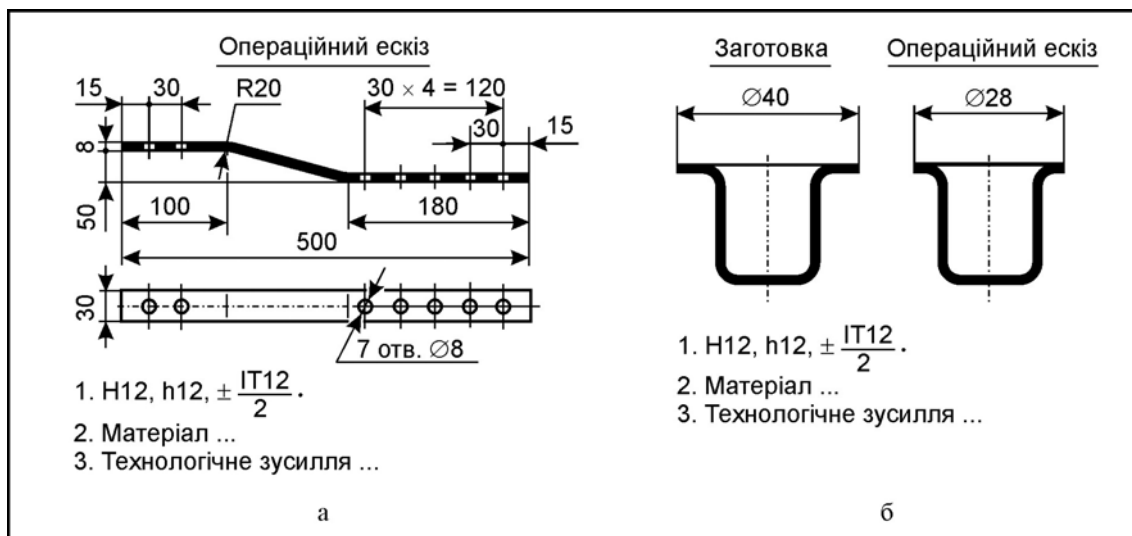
Приклади оформлення операційних ескізів: а – операційний ескіз деталі «Планка» штампа для пробивання; б – ескіз вихідної заготовки (ліворуч) та та операційний ескіз (праворуч) деталі «Ковпачок» штампа для обрізування
